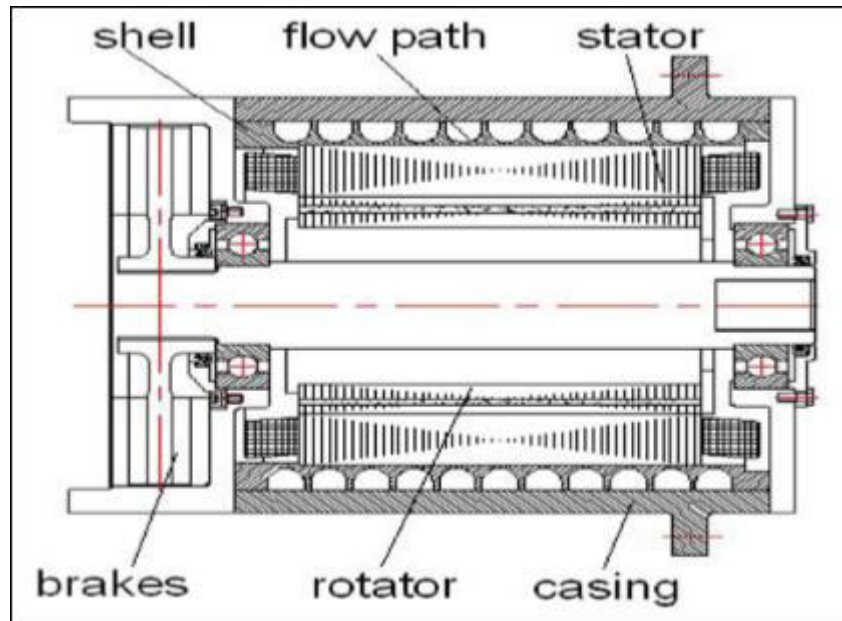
Moteur avec le trajet d'écoulement en forme spirale intégré à la coque et à l'extérieur du stator.
